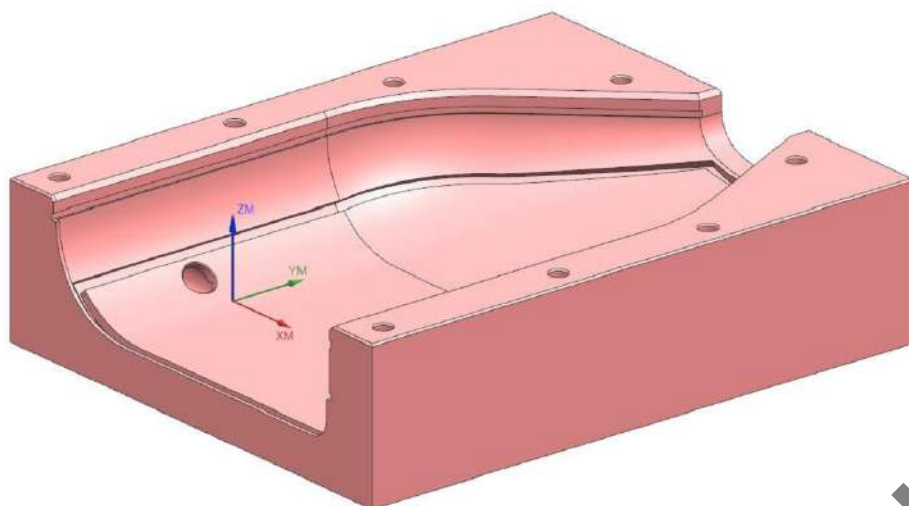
3D-модель вакуумного зажимного приспособления
